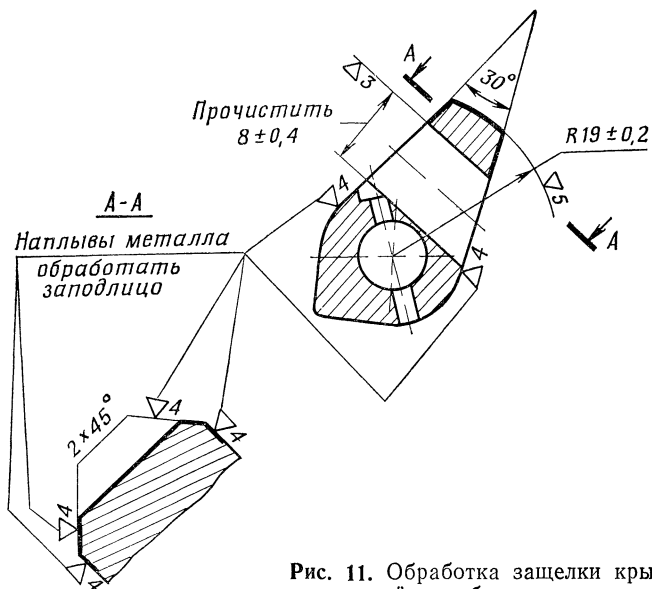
Обработка защелки крышки ствольной коробки после наплавки
